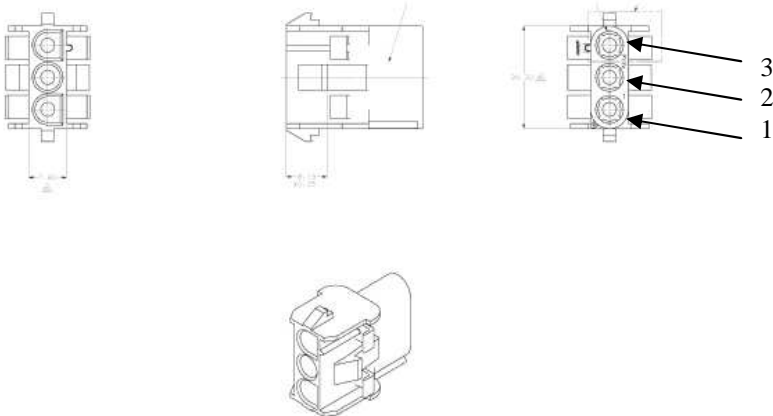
Conector Universal MATE-N-LOK de 3 circuitos Cap Housing (fêmea).
